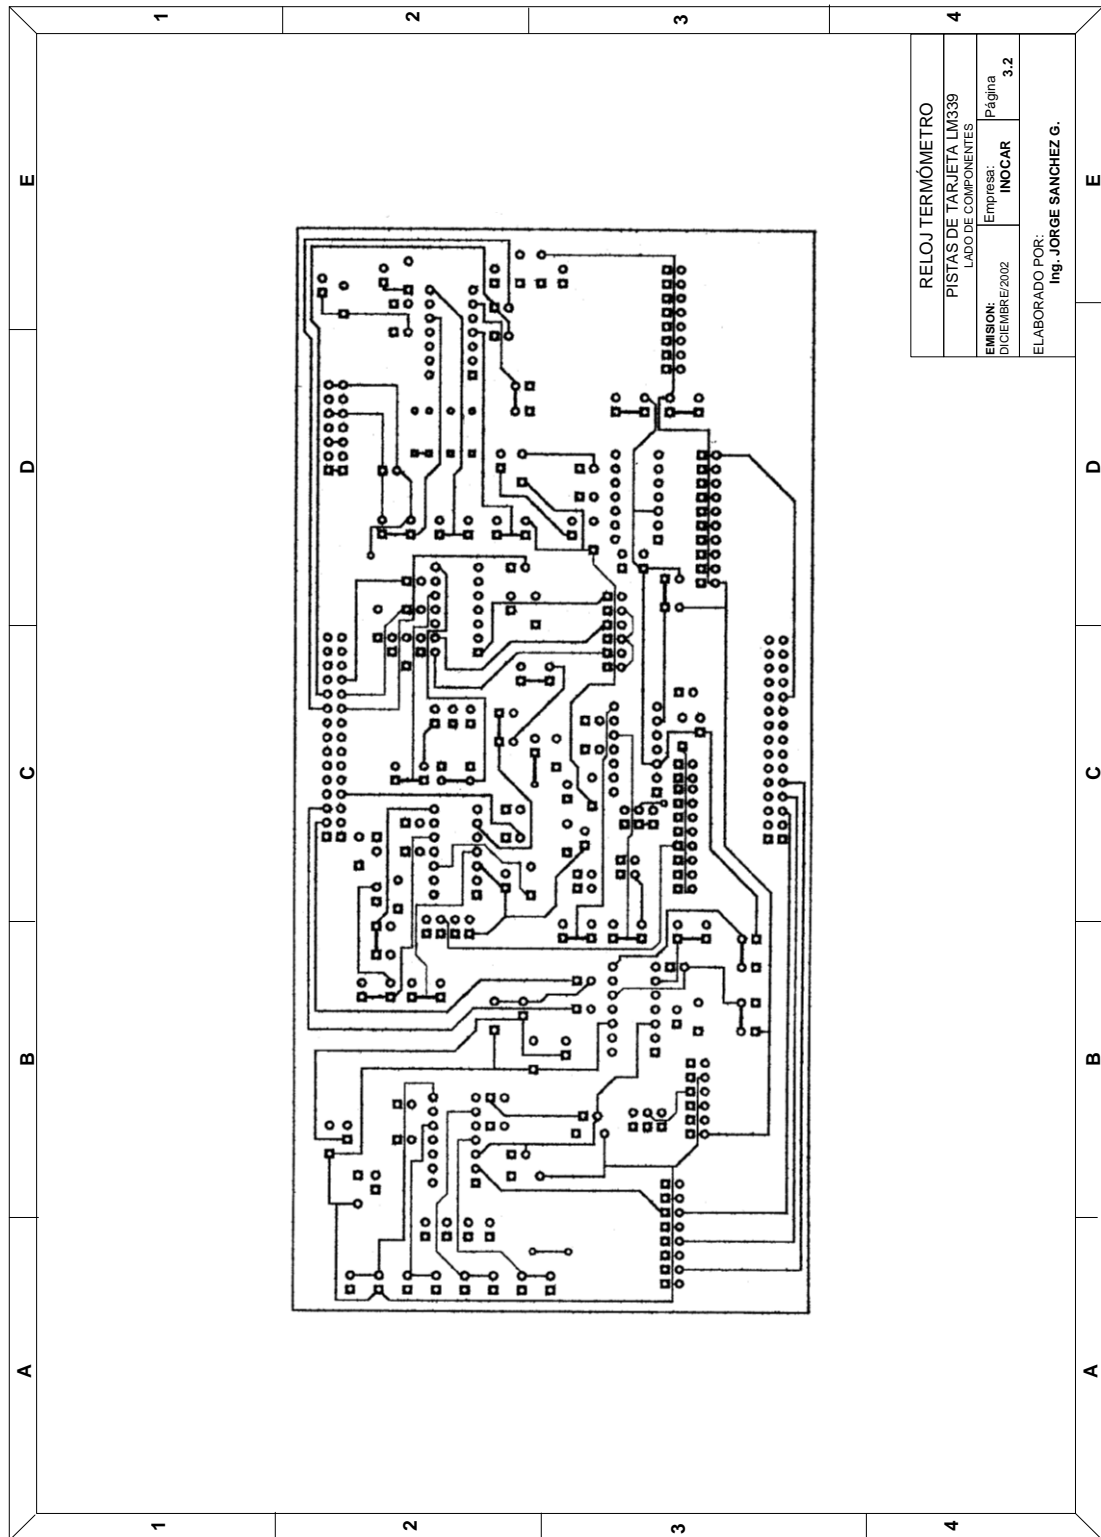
Tarjeta LM 339 (Diagrama de pistas lado de soldadura)
